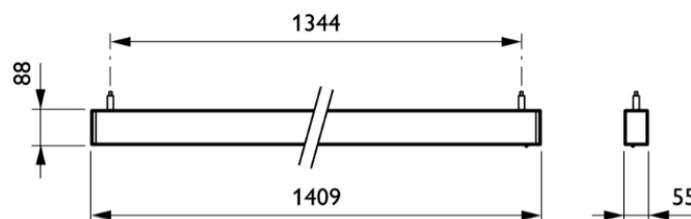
Plano de Dimensiones Luminaria TrueLine Suspendida
